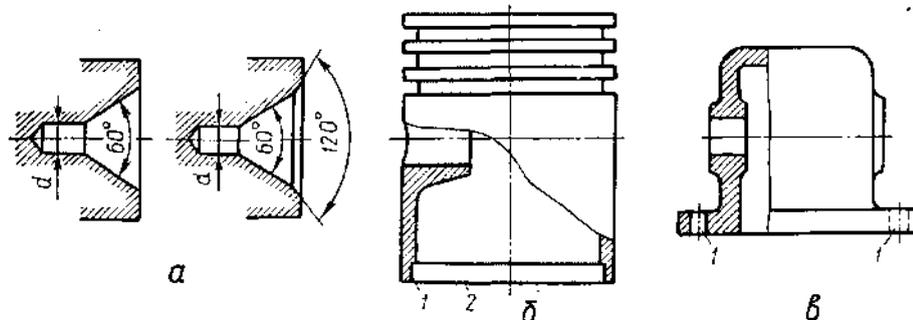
Допоміжні технологічні бази: *a* — центрувальні отвори (звичайне і з запобіжним конусом 120°); *б* — пасок поршня, що центрує; *в* - установочні отвори в корпусній деталі
